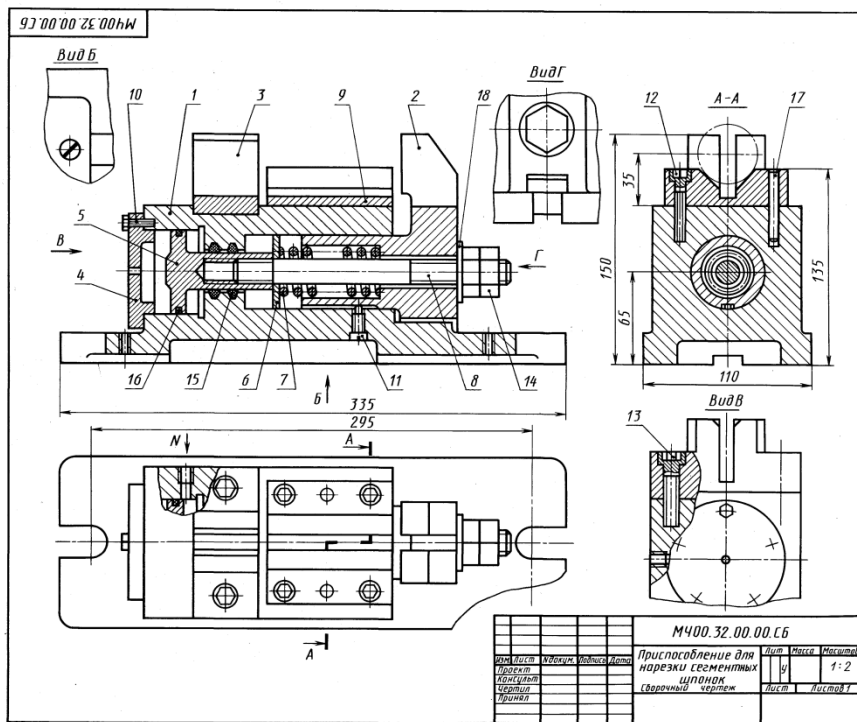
Сборочный чертеж «Приспособление для нарезки сегментных шпонок»
